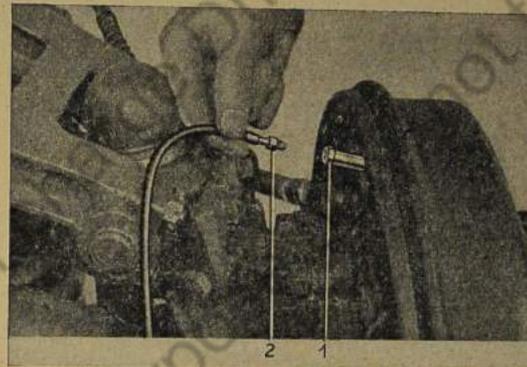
Entlüftungsschlauch in Entlüftungsventil einschrauben
